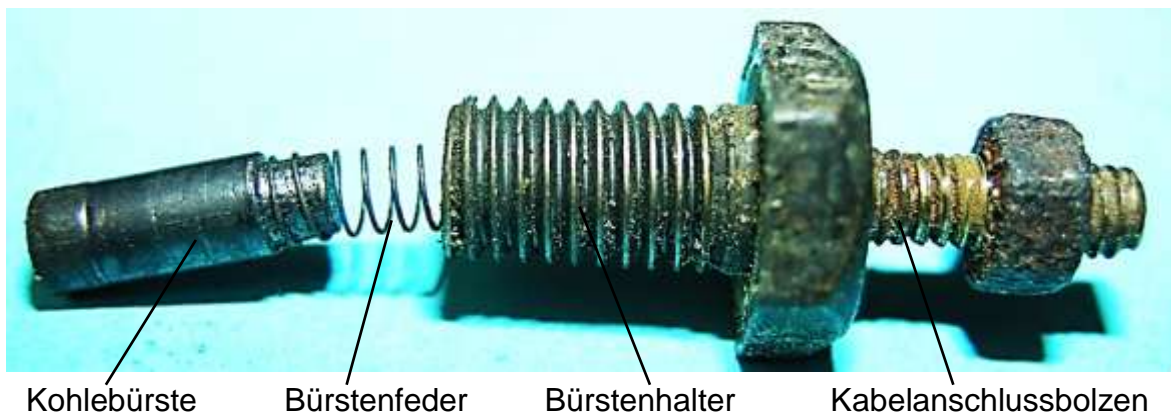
Bürstenhalter in Kombination mit dem Kabelanschlussbolzen
